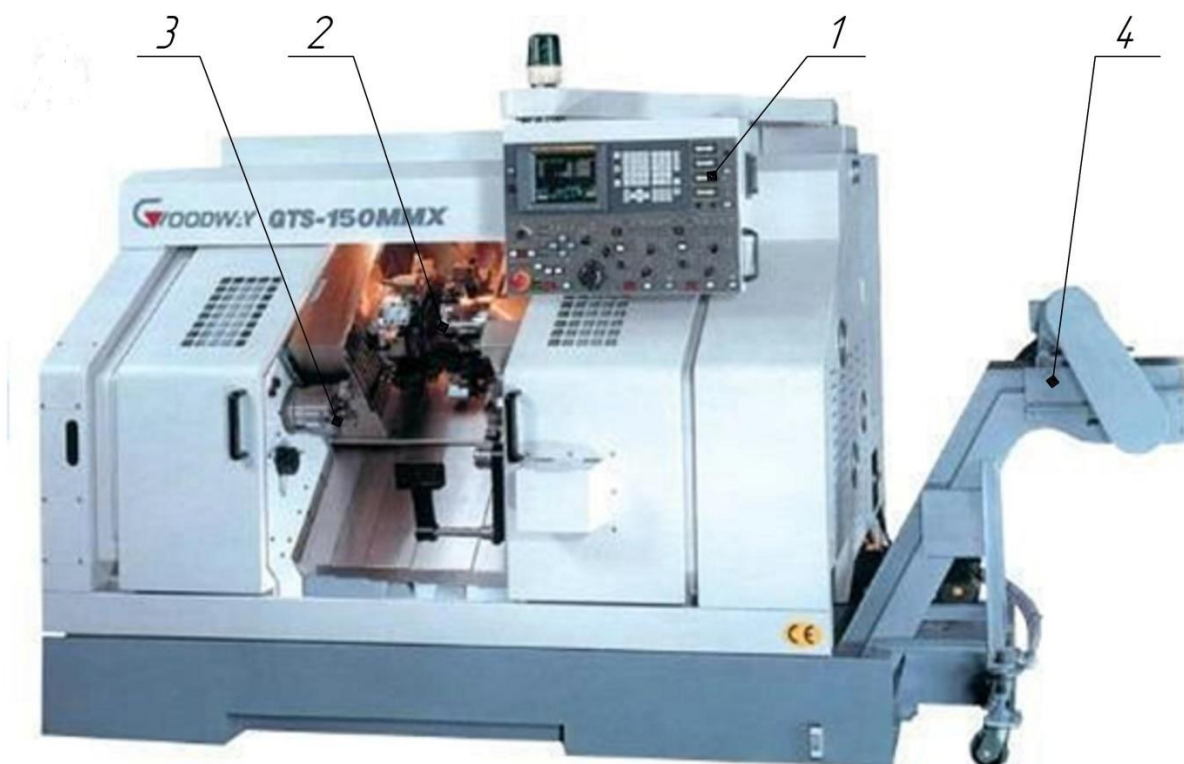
Одношпindelний токарно–револьверний автомат:
